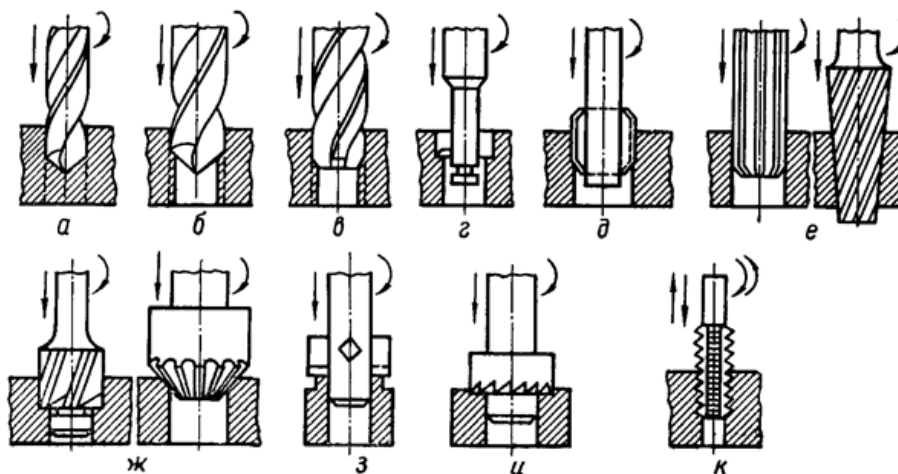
Схеми обробки поверхонь на вертикально - свердлильному верстаті:
